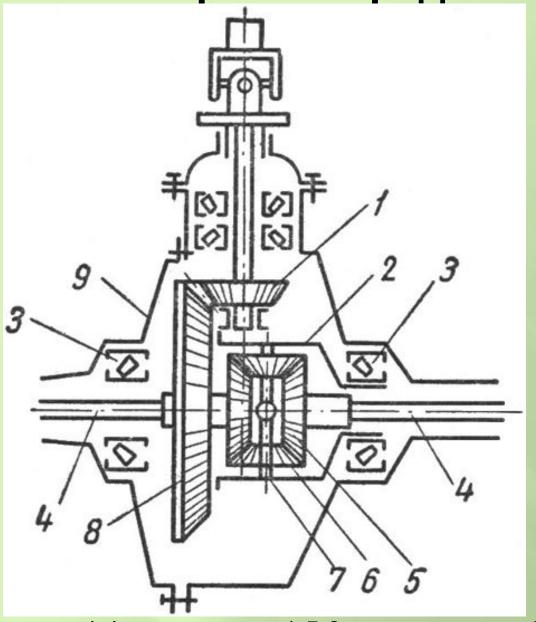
Схема дифференциала: 1,5,8 – шестерня; 3 – подшипник; 4 – полуось; 6 – сателлит
